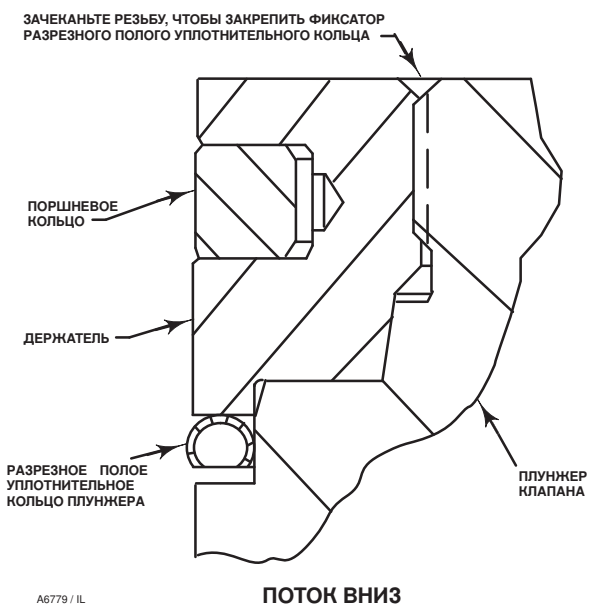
Закрепление резьбовых соединений фиксатора разрезного полого уплотнительного кольца
